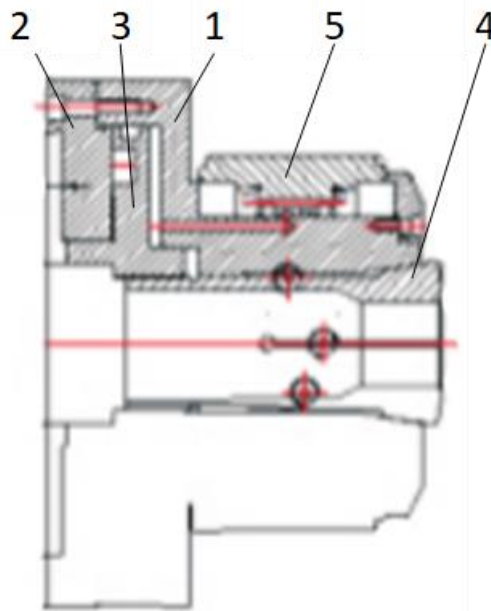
Гідравлічний цанговий затискний патрон з цангою тягнучого типу серії JHB фірми DRAKE PRECISION TECHNOLOGY
